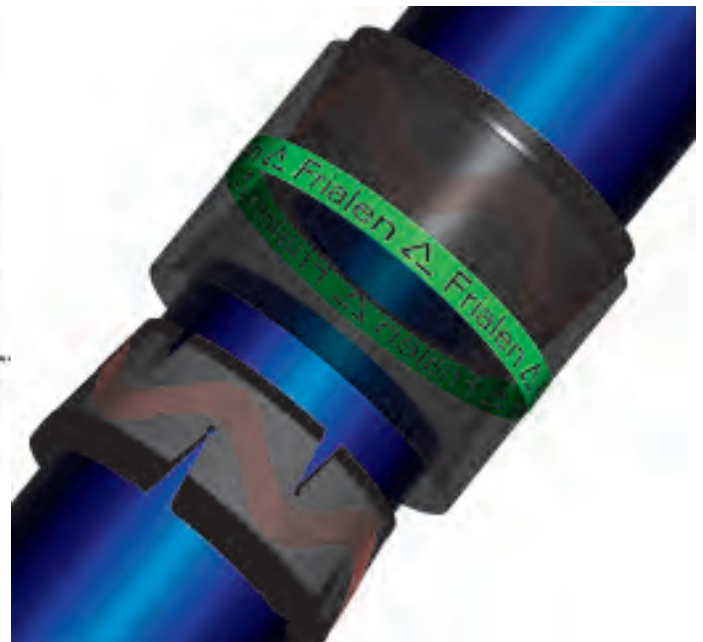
Соединительная муфта, состоящая из двух конических сварочных втулок и корпуса. Нижняя – перед сборкой, верхняя – в окончательном положении.
